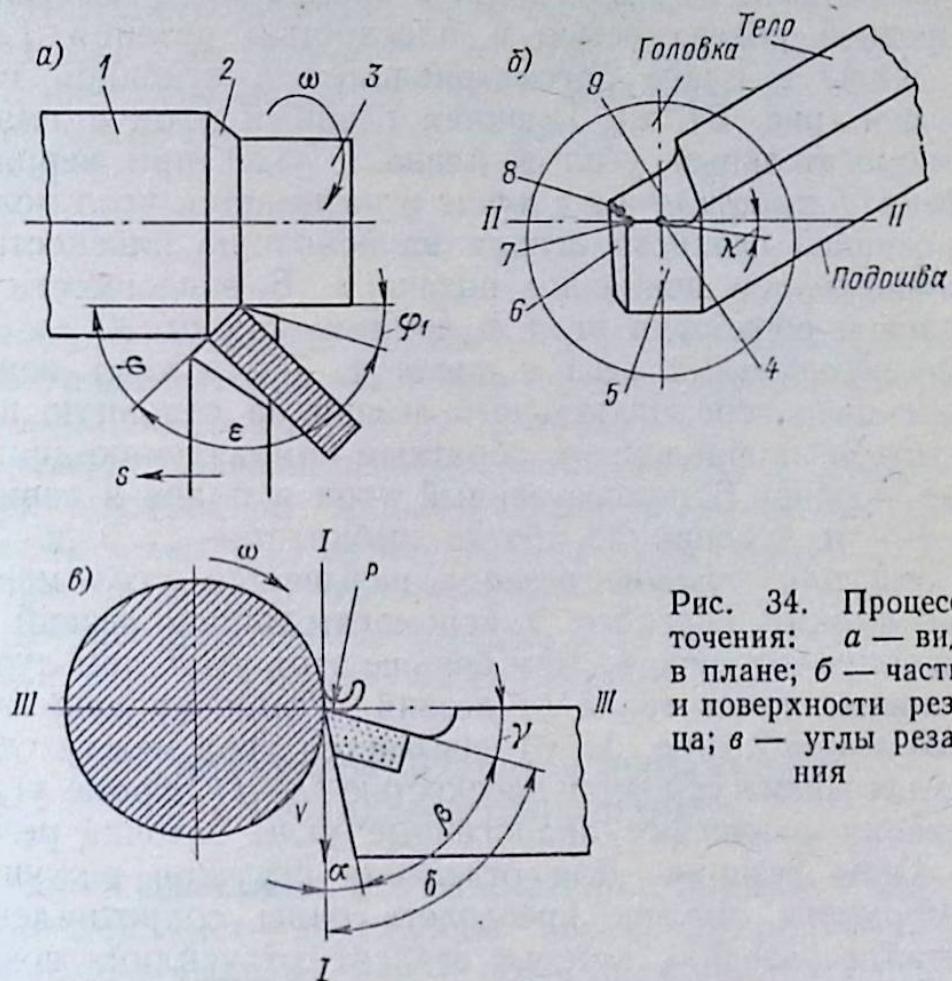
Процесс точения: а — вид в плане; б — части и поверхности резца; в — углы резания
